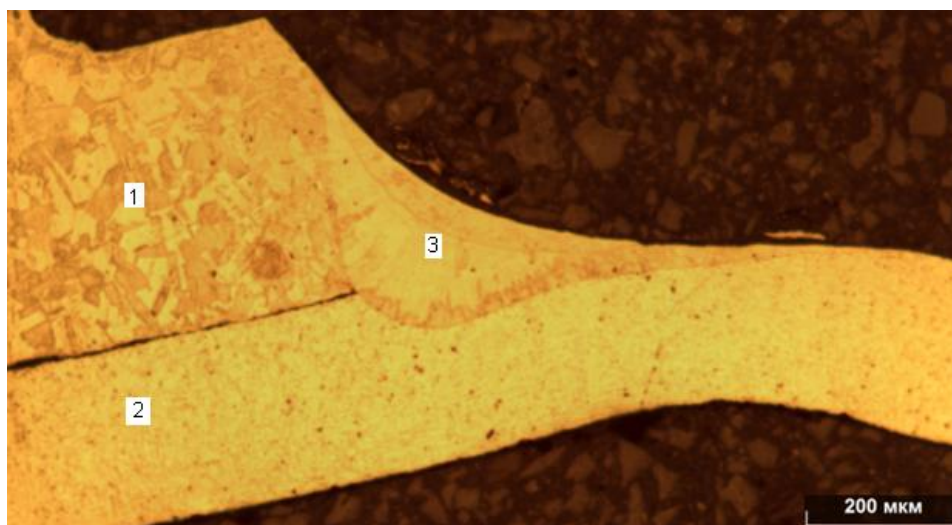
Поперечное сечение сварного шва при сварке по исходному варианту, мощность лазерного излучения при сварке 700 Вт:
